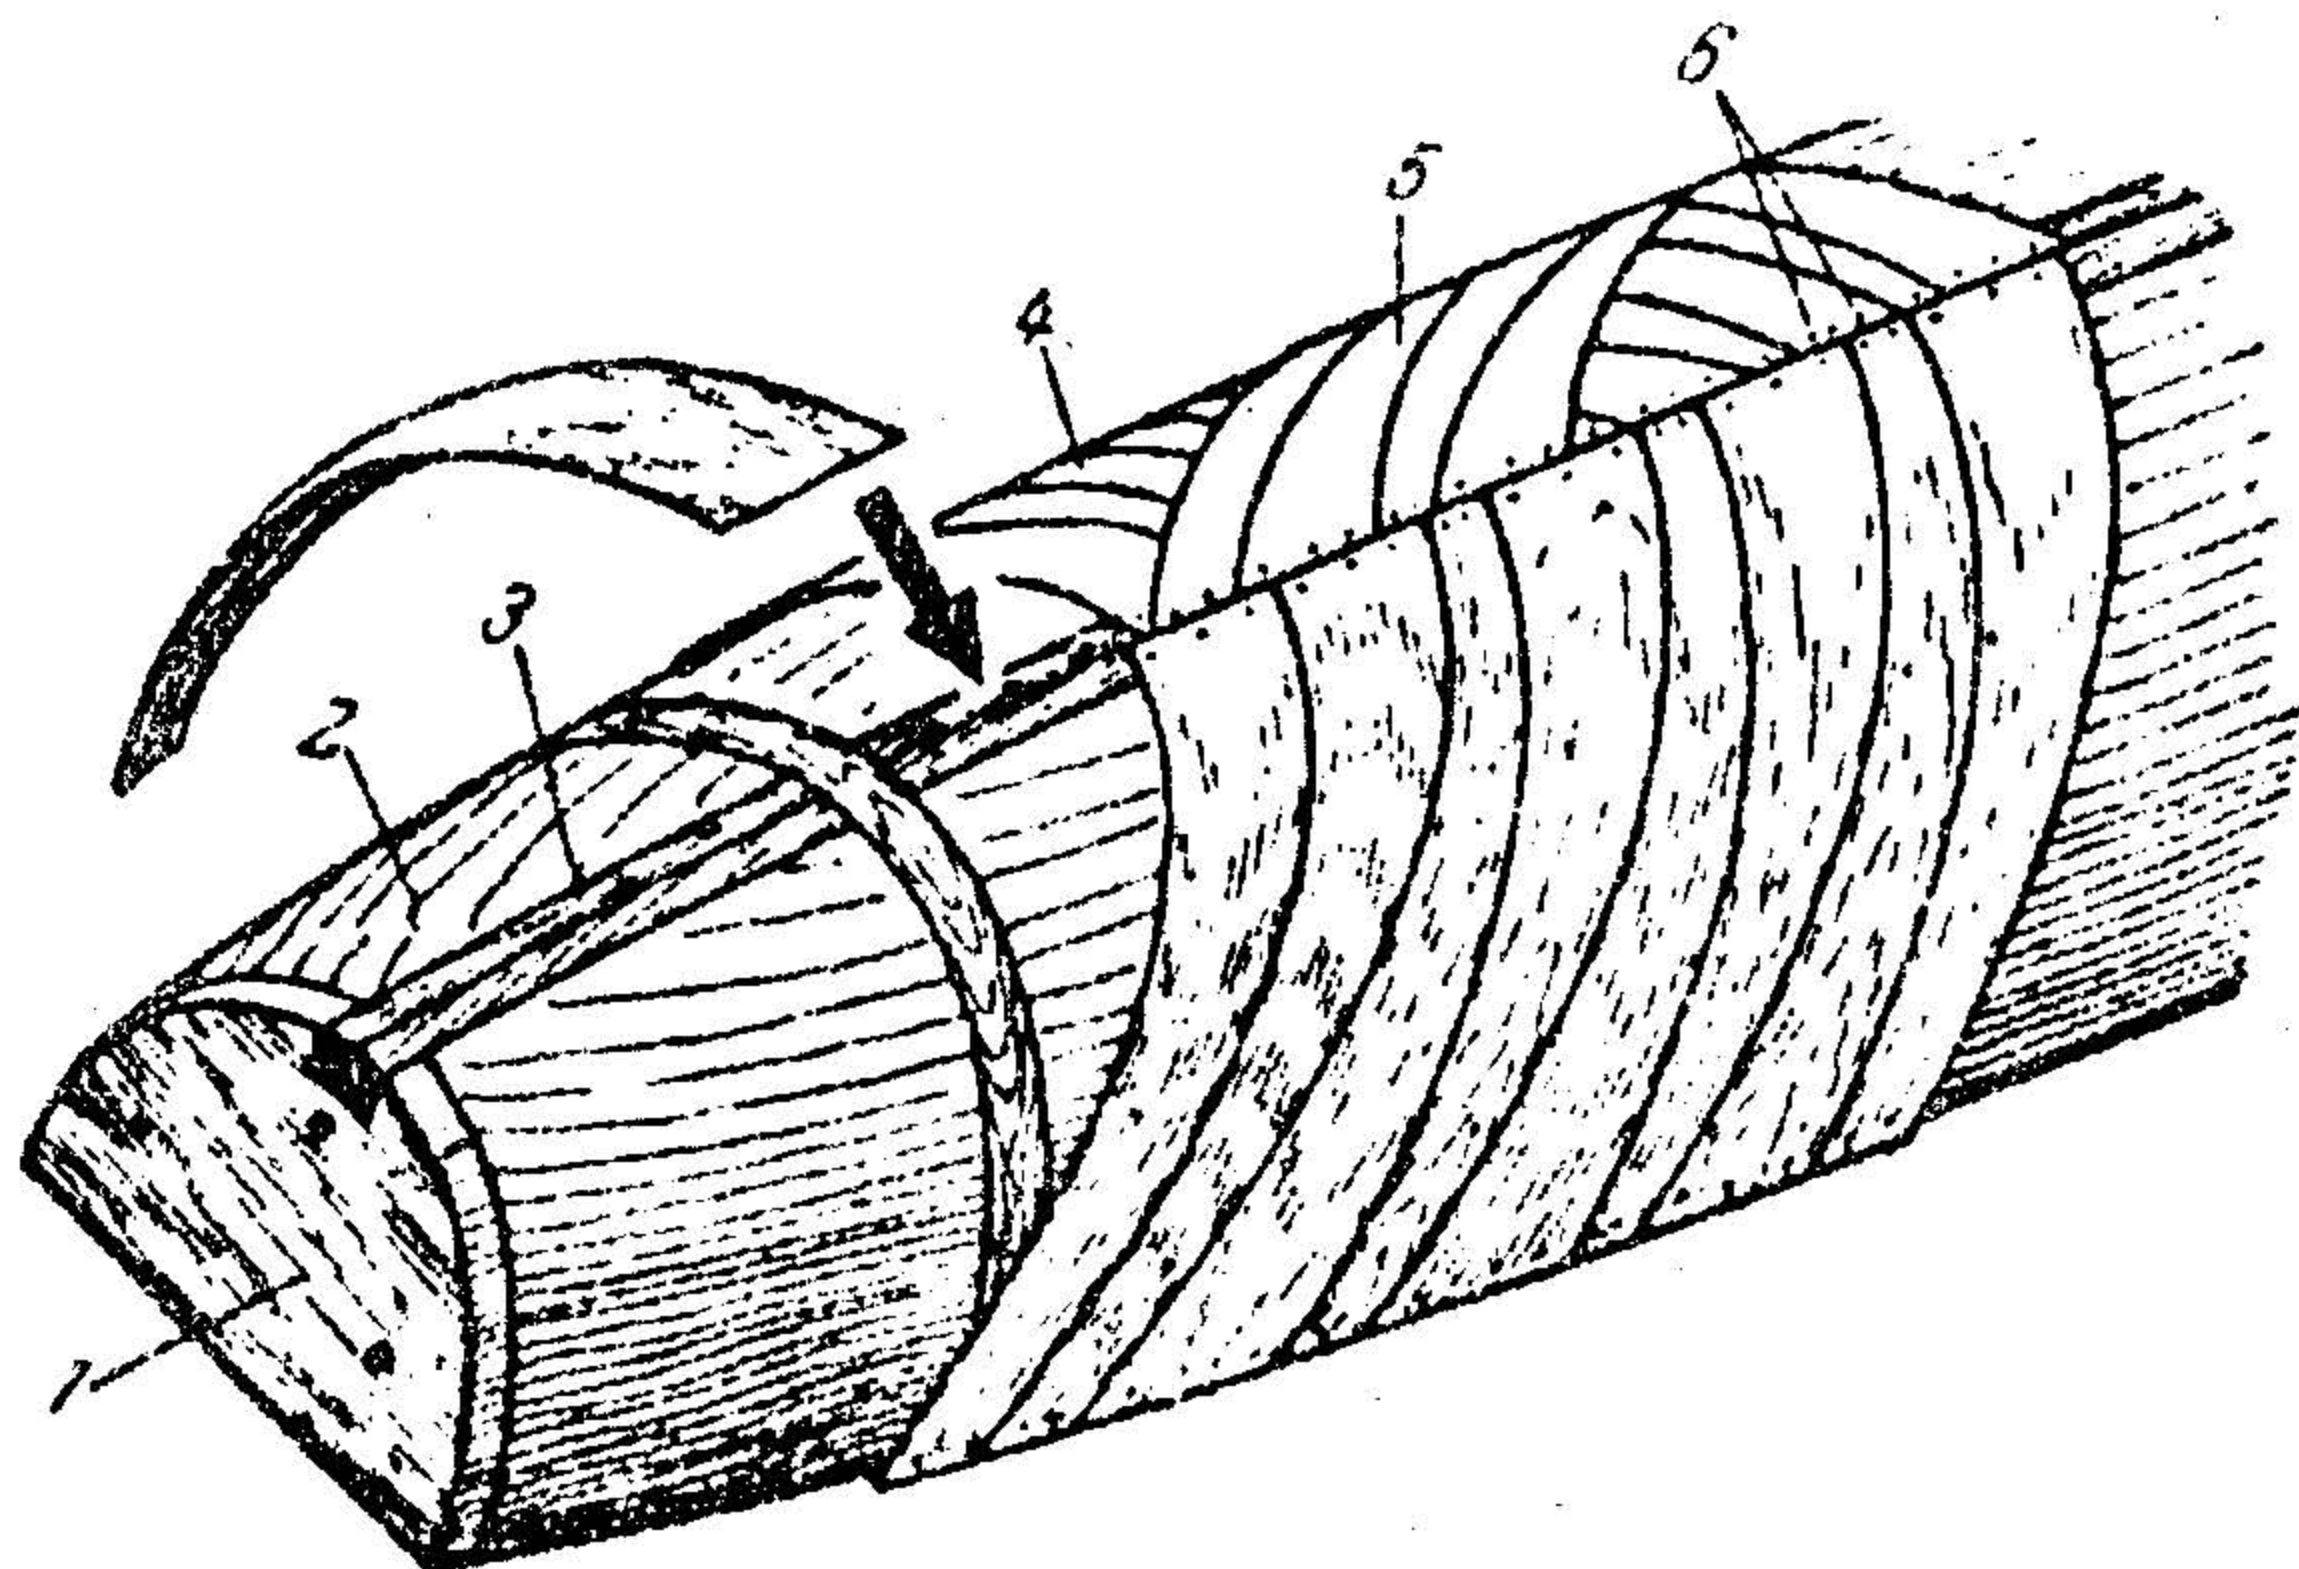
Обшивка корпуса: 1 — транцевая доска; 2 — болванка; 3 — киль; 4 — первый слой диагональной обшивки; 5 — второй слой диагональной обшивки; 6 — гвозди
